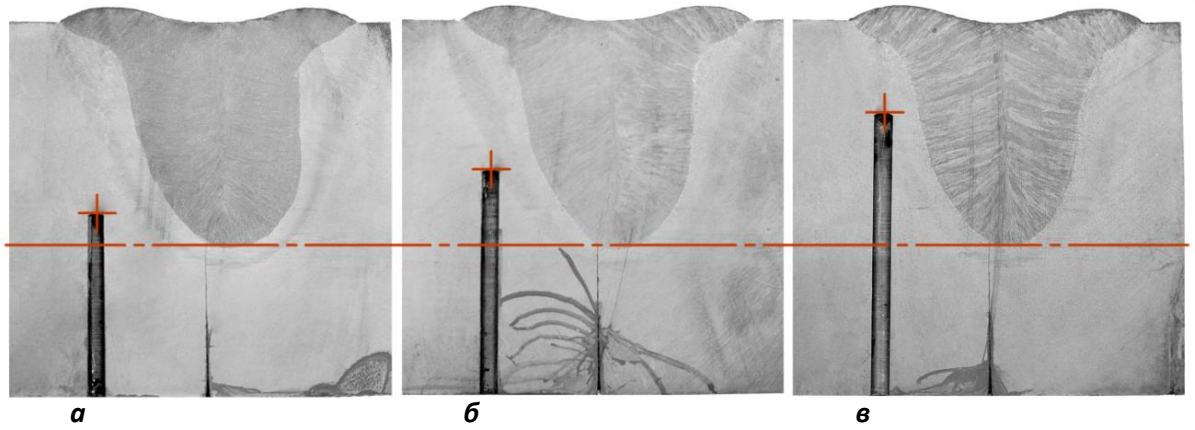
Макрошлифы сварного соединения, вырезанные перпендикулярно оси шва в плоскостях расположения отверстий.
